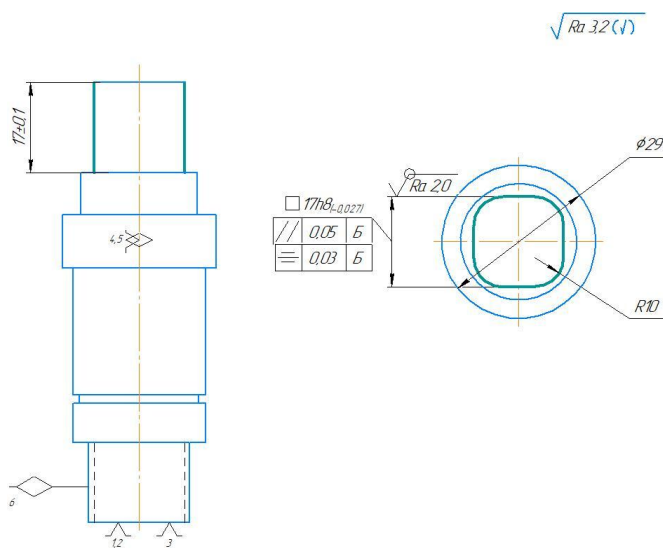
схема установки заготовки в приспособление(Установ Б).
